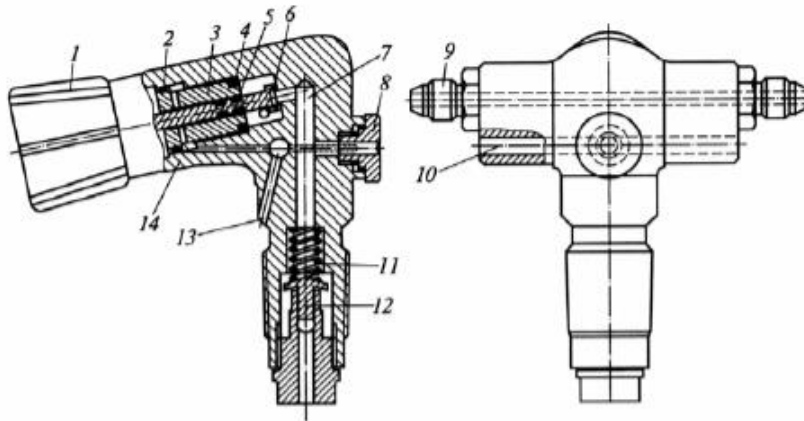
Вентиль баллонный для дренажной схемы подключения:
